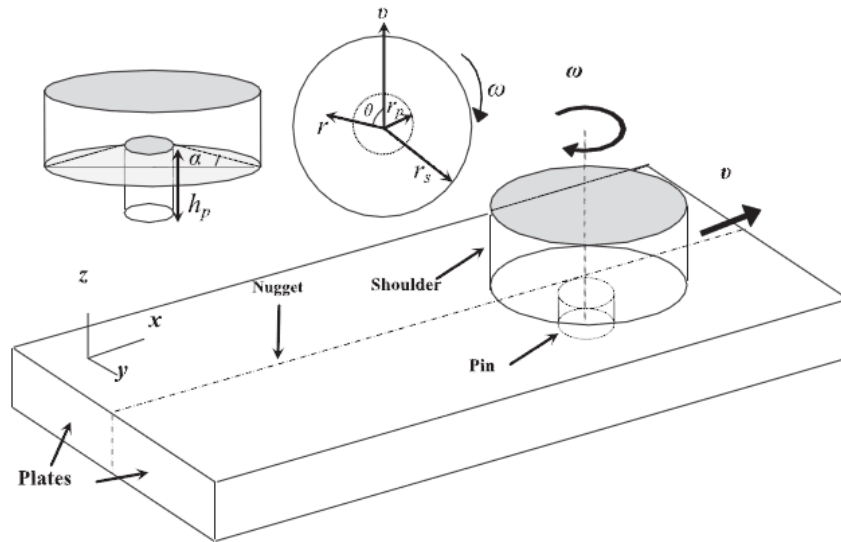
2 Representación esquemática de la soldadura por fricción batido y parámetros
